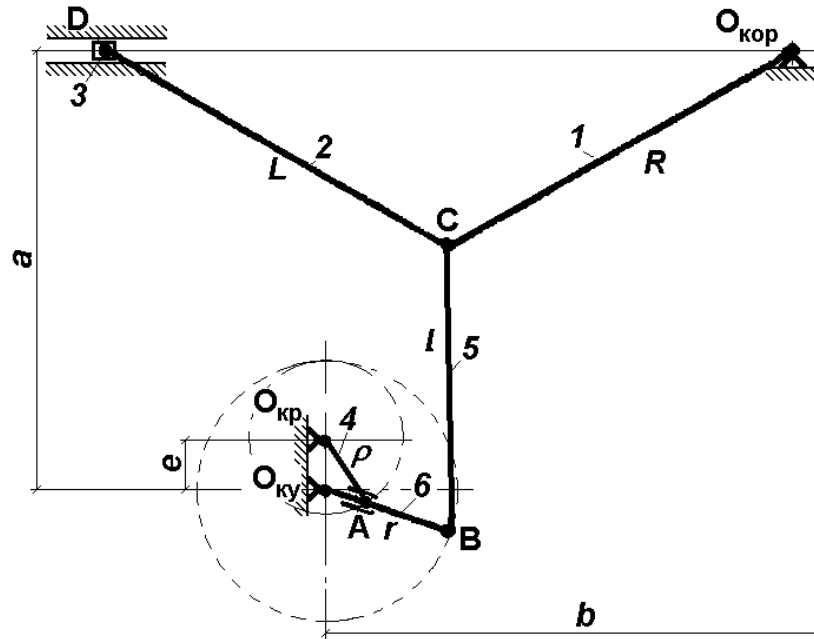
Кінематична схема кулісного коромисло-повзунного преса-брикетувальника: 1 - коромисло; 2 - шатун поршня; 3 - поршень; 4 - кривошип; 5 - шатун кривошипа; 6 – куліса.
